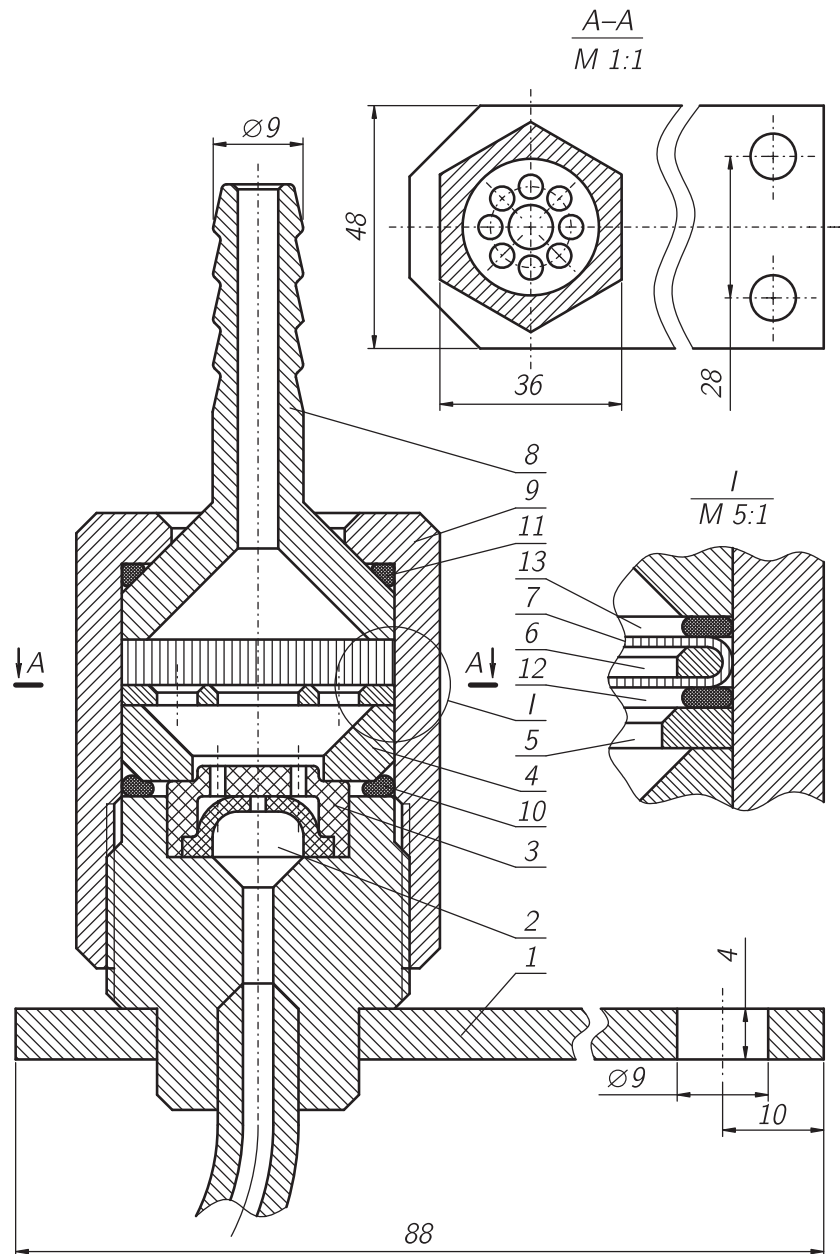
Разработанный фильтр: 1 — корпус; 2 — клапан-отсекатель; 3 — седло клапана; 4 — втулка; 5 — шайба поддерживающая; 5 — кольцо; 7 — ткань фильтровальная; 8 — нипель; 9 — гайка накидная; 10, II, 12, 13 — кольца уплотнительные резиновые
